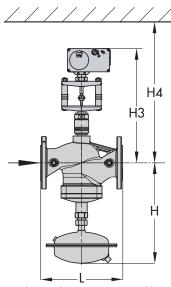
Dimensions des régulateurs, vanne équilibrée par membrane
